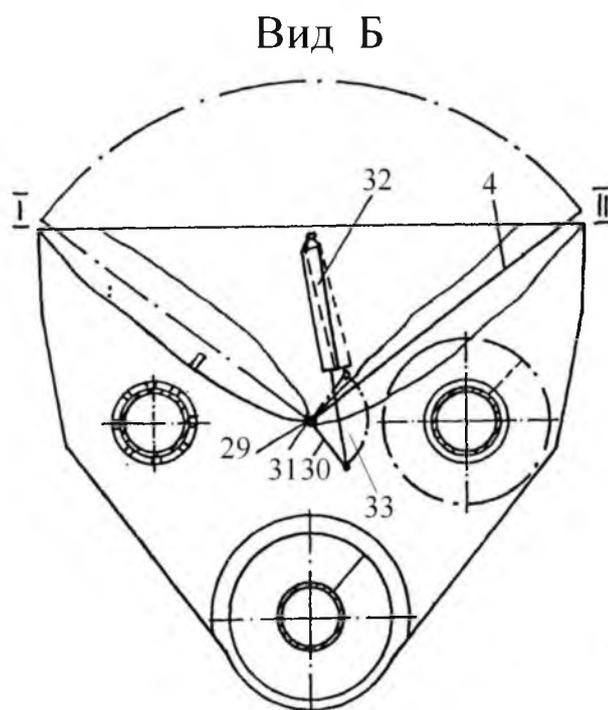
Мобильный кормоприготовительный агрегат (вид Б на рис. 2):
